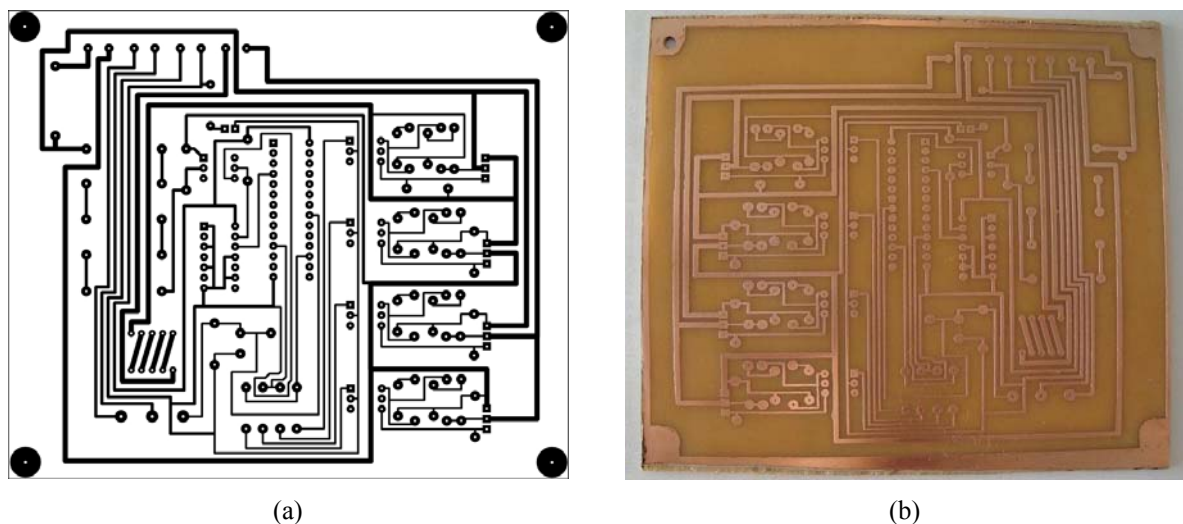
Placa de circuito impresso utilizada no projeto: (a) *layout* da placa; (b) placa finalizada.
